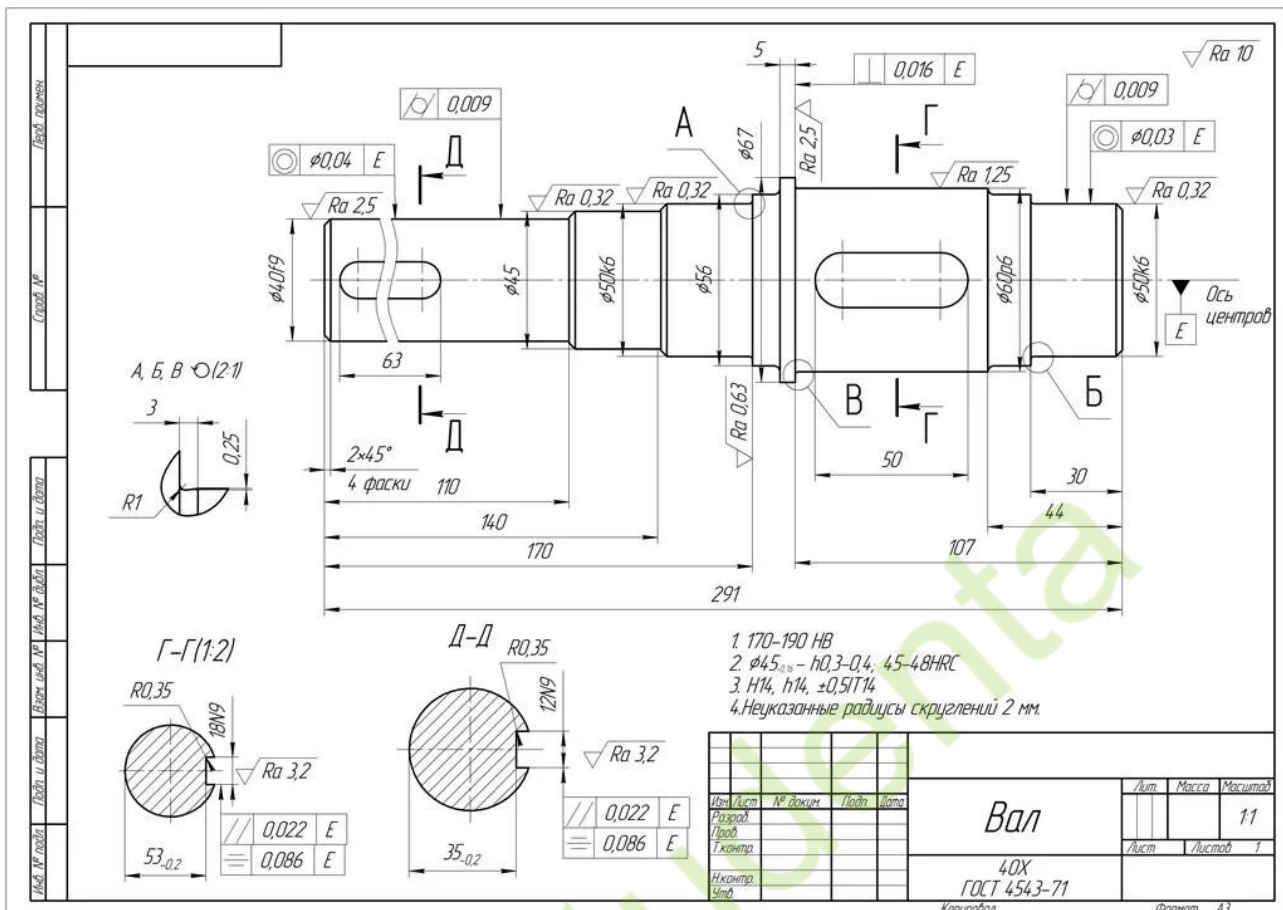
Чертёж детали вал ООО «АКВАФИЛД»
